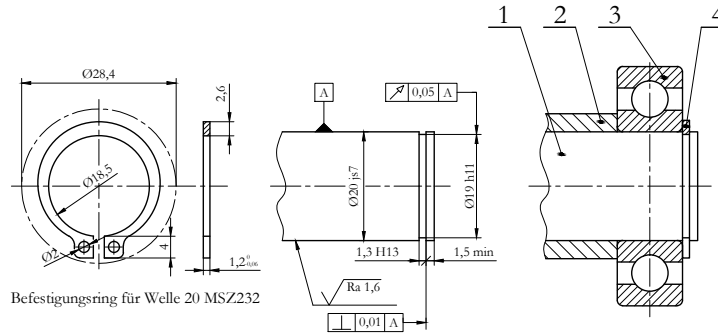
Standard-Befestigungsringe für Wellen/Achsen
